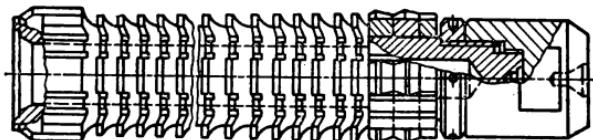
Прошивка шлицевая сборная режуще-выглаживающая
